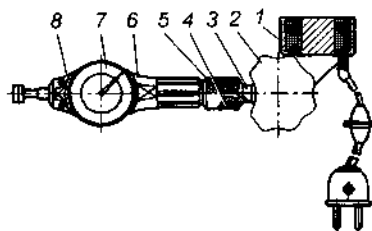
Устройство КИ-8902А для проверки биения карданных валов на автомобиле: 1 — электромагнит; 2 — рукоятка; 3 — рычаг; 4 — сухарик; 5 — зажим; 6 — корпус; 7 — индикатор; 8 — крышка
